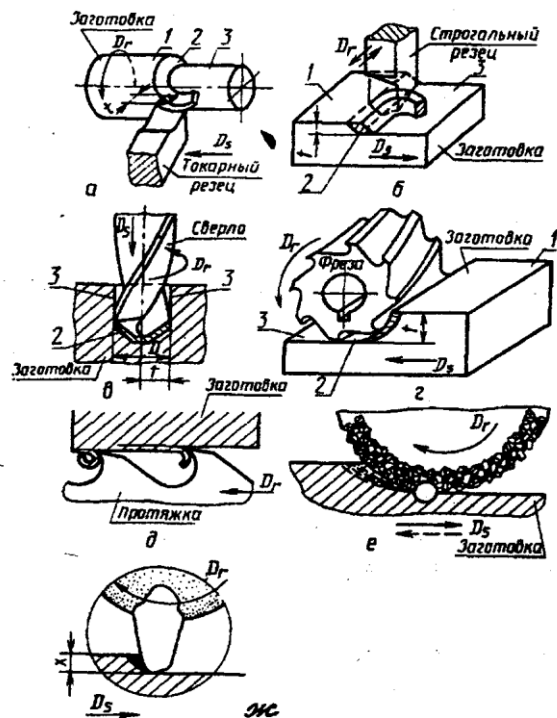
Схеми основних видів обробки різанням: а) точіння; б) стругання; в) свердління; г) фрезерування; д) протягування; е) шліфування; є) зняття стружки окремим абразивним зерном; 1 – оброблювана поверхня; 2 – поверхня головного руху різання; 3 – оброблена поверхня; t – припуск; D_s – рух подачі; D_r – головний рух різання
